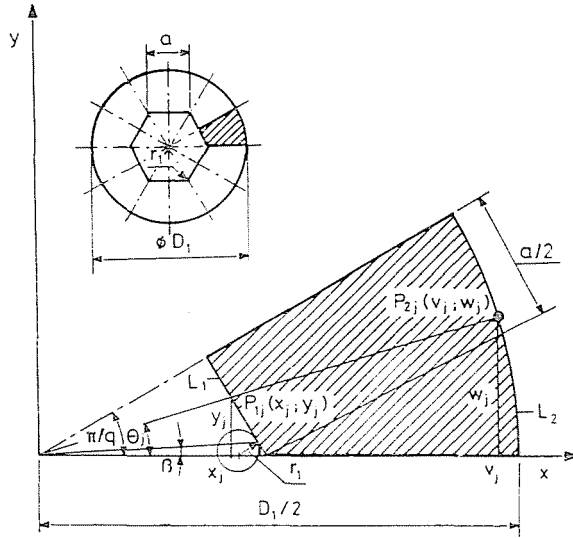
Das berücksichtigte Segment einer Matrize mit hexagonaler Werkzeugöffnung
